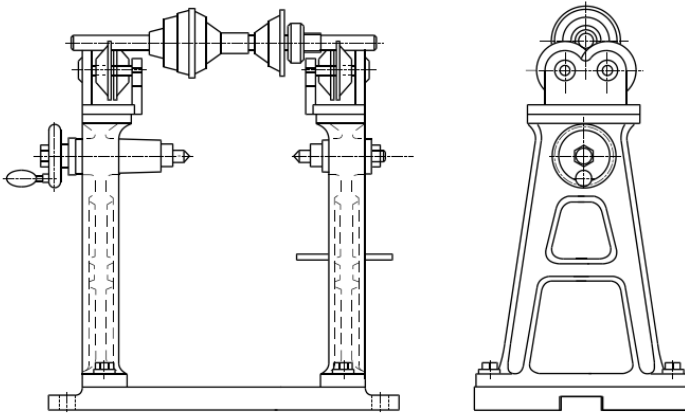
Пристрій для статичного балансування і перевірки в центрах дрібних деталей.
